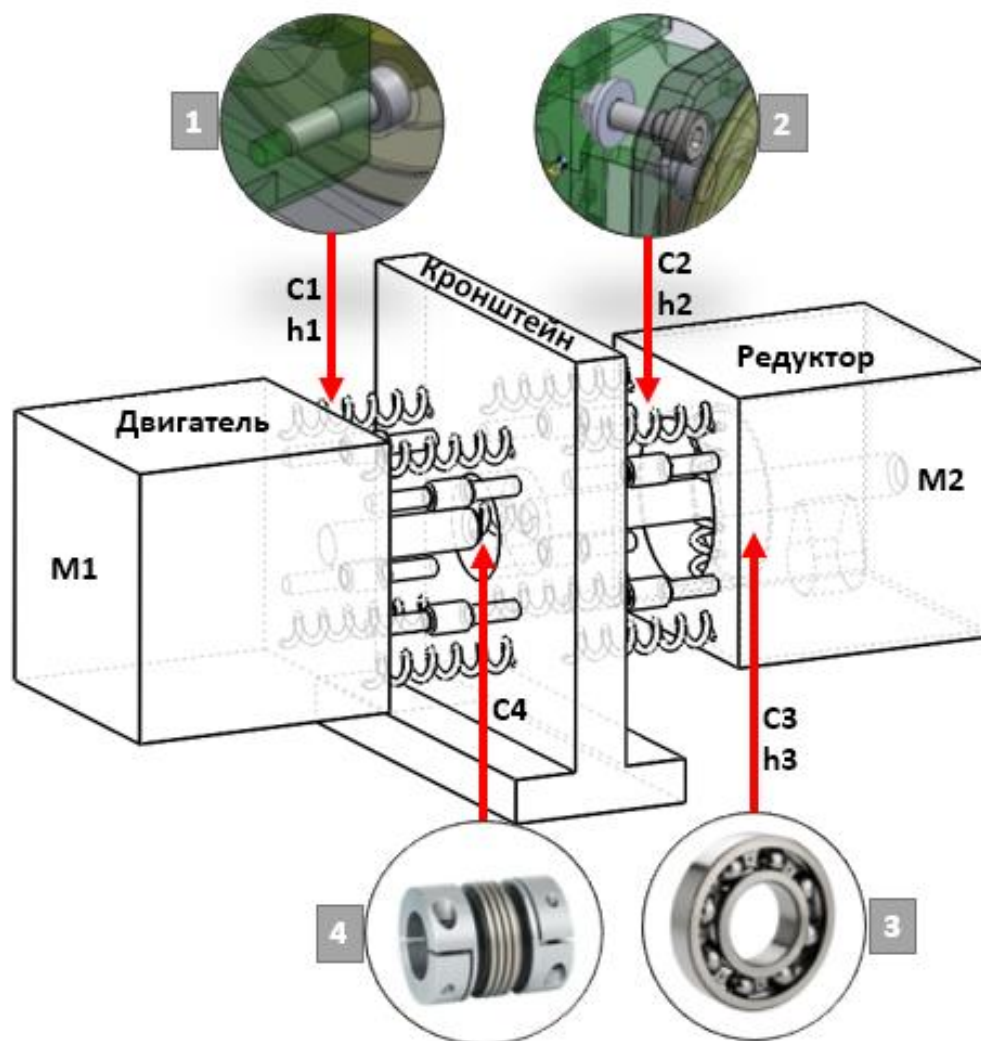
Схема монтажа редуктора и его компонентов.
